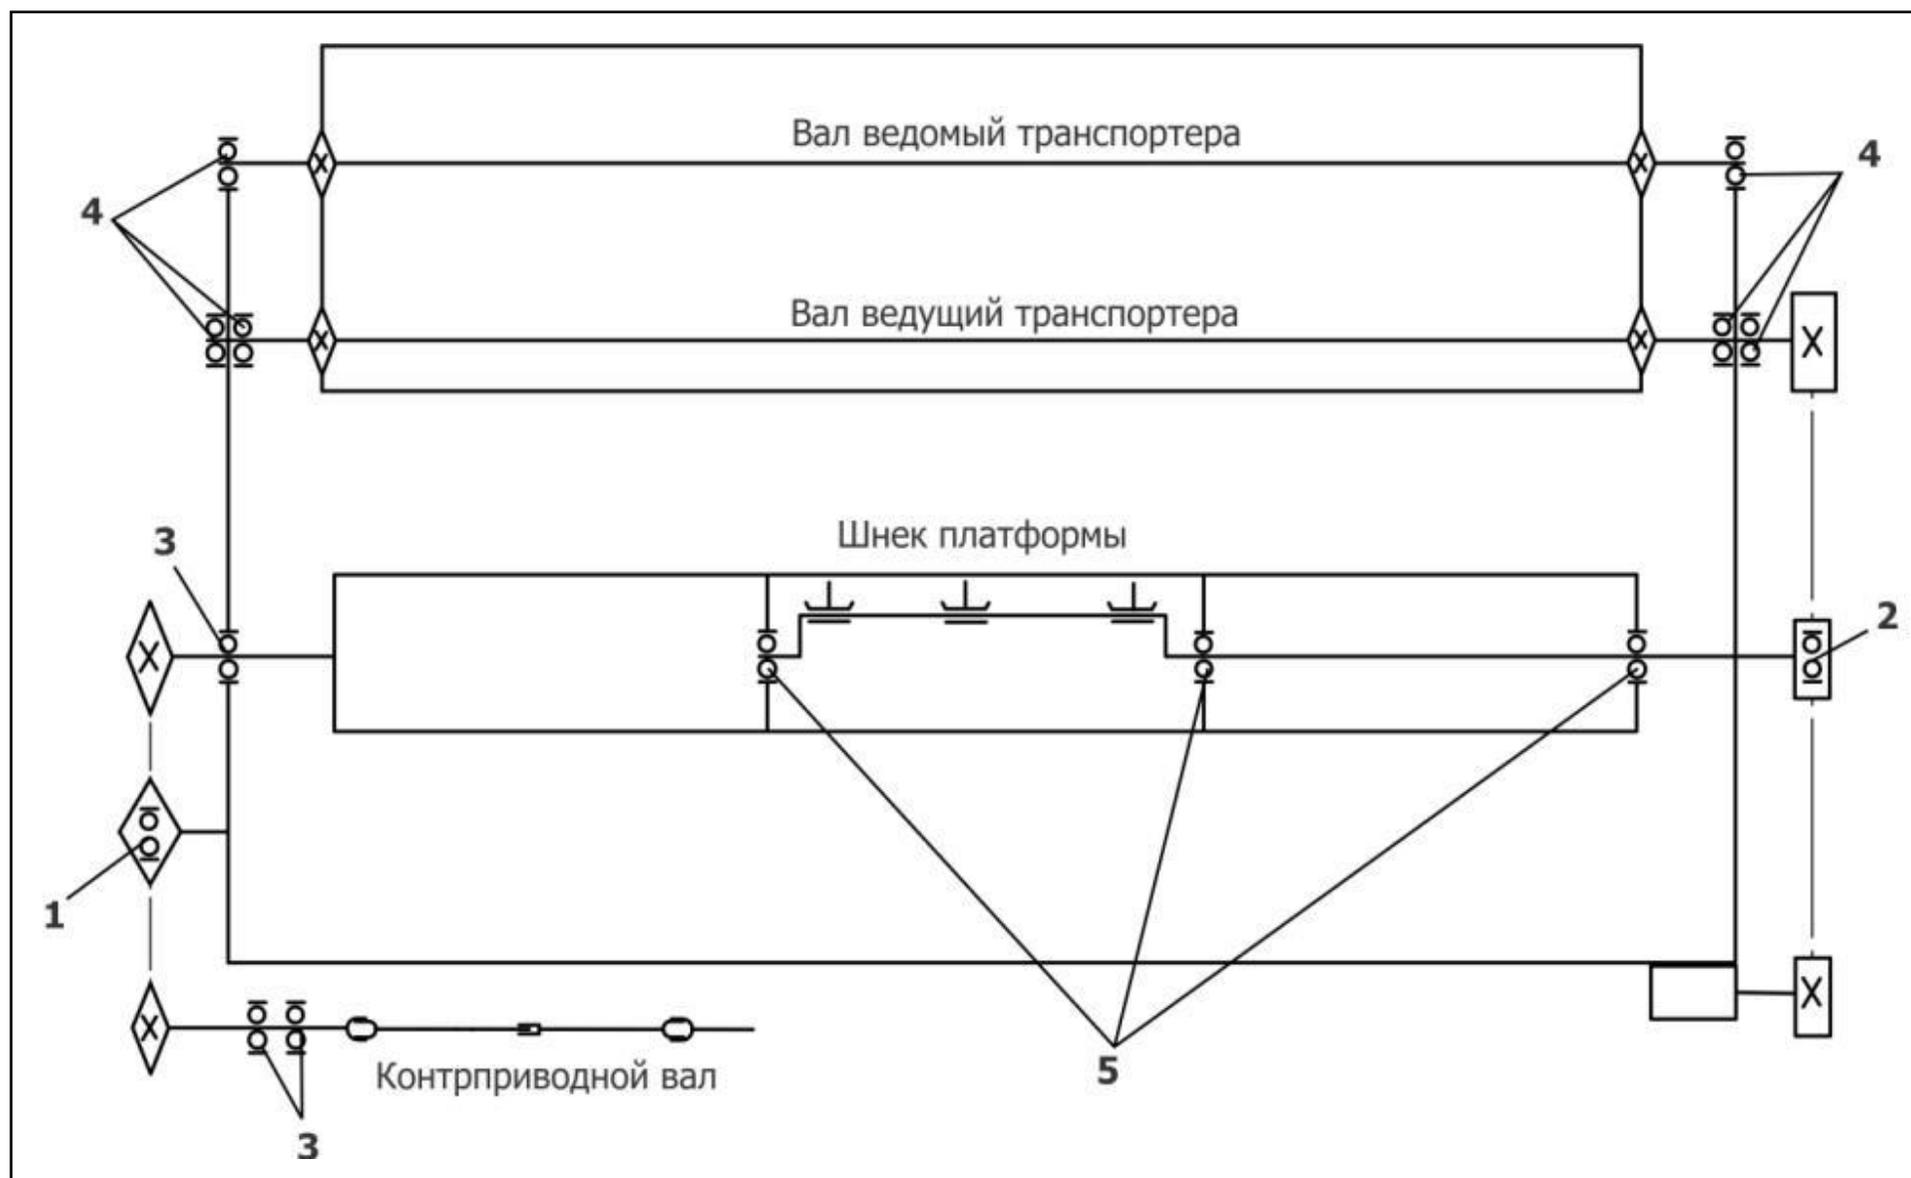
Схема расположения подшипников платформы-подборщика
